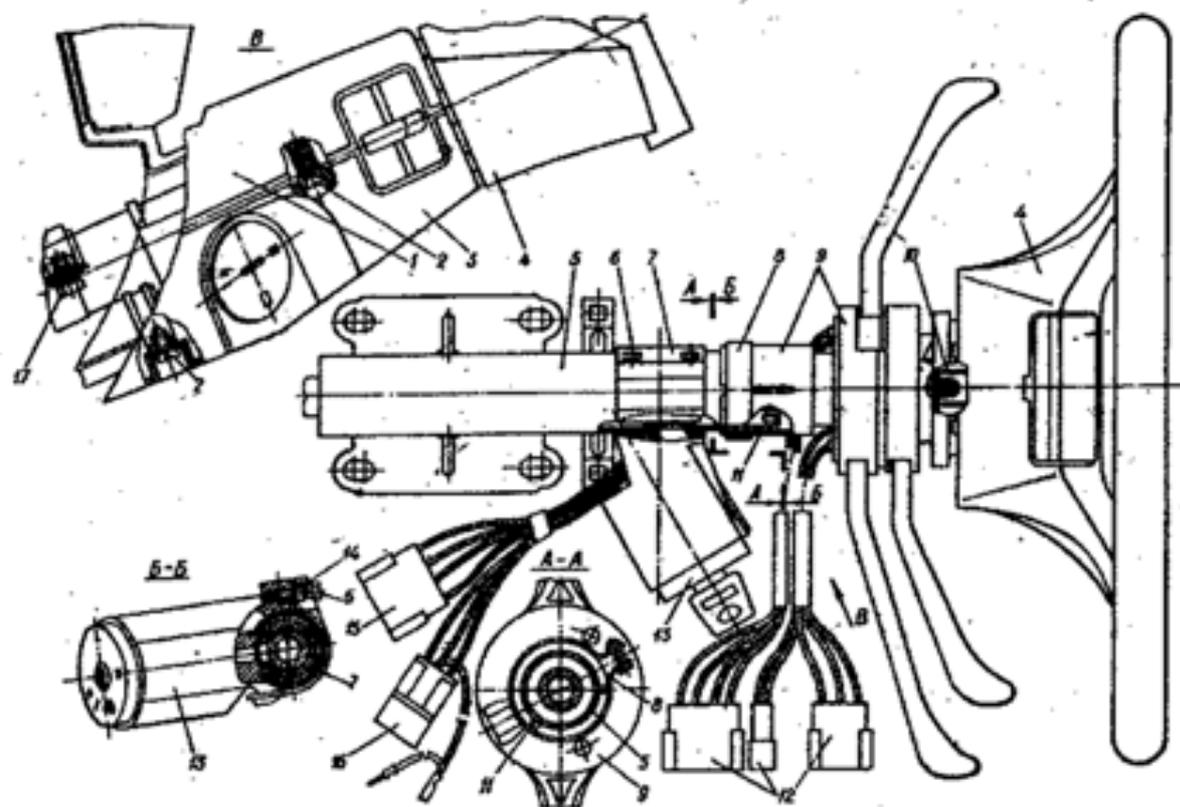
Опора вала в сборе: 1 - кожух верхний; 2 - винт; 3 - кожух нижний; 4 - колесо рулевое; 5 - опора вала; 6 - головка болта; 7 - скоба; 8 - хомут; 9 - переключатель в сборе; 10 - выступ на кольце сбрасывателя; 11 - выступ на опоре вала; 12 - штекерные колодки переключателя; 13 - выключатель зажигания; 14 - болт; 15 - штекерная колодка; 16 - реле выключателя зажигания; 17 - болт крепления опоры.
